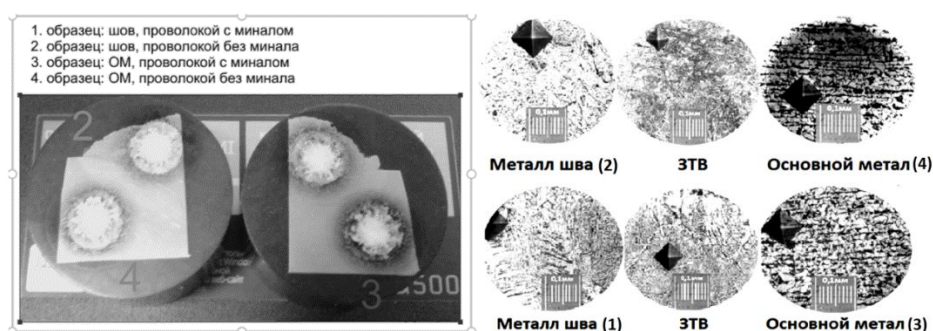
Макро- и микрошлифы наплавленного металла
